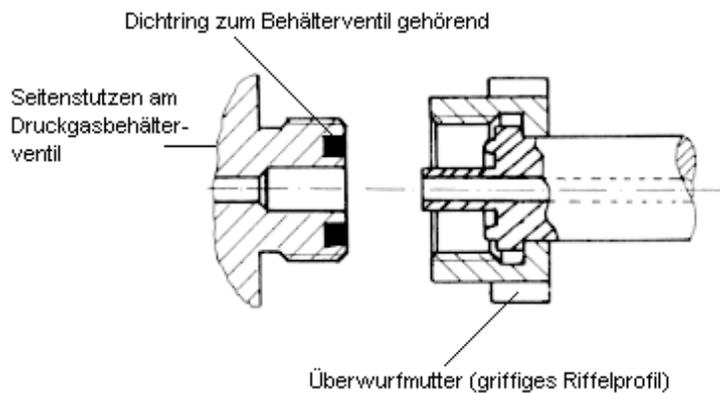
Anschluß für Druckgasbehälter mit einem zulässigen Füllgewicht bis 14 kg
